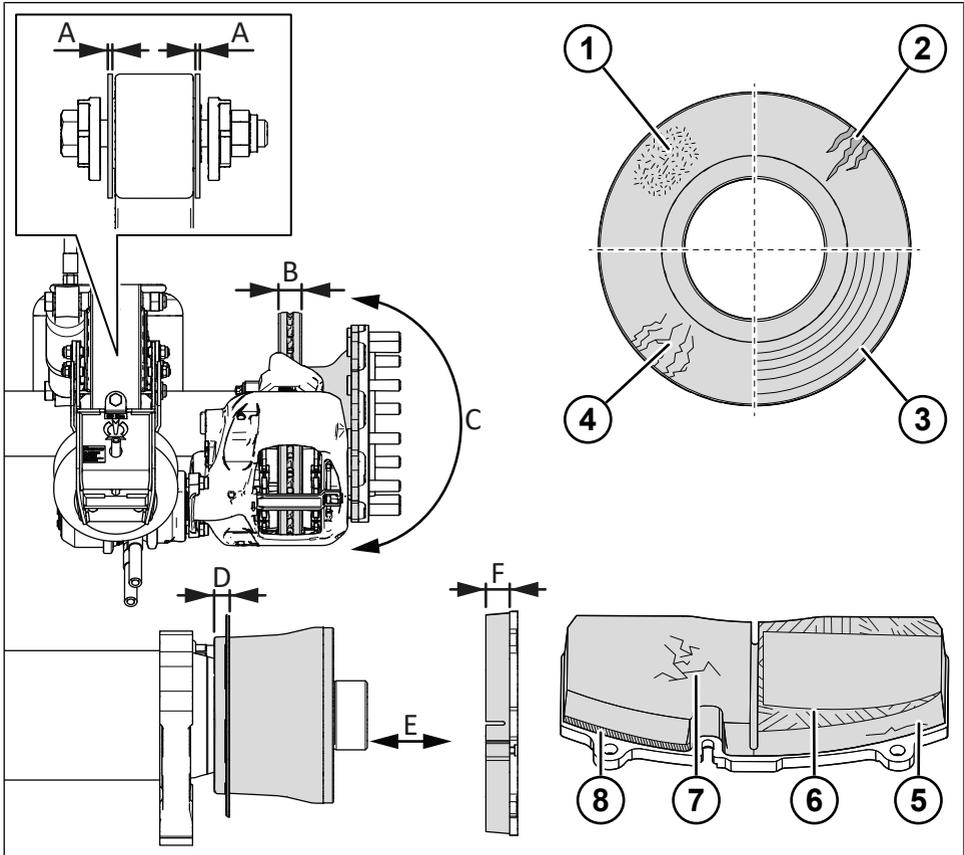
Vue d'ensemble des cotes d'usure et de réglage
